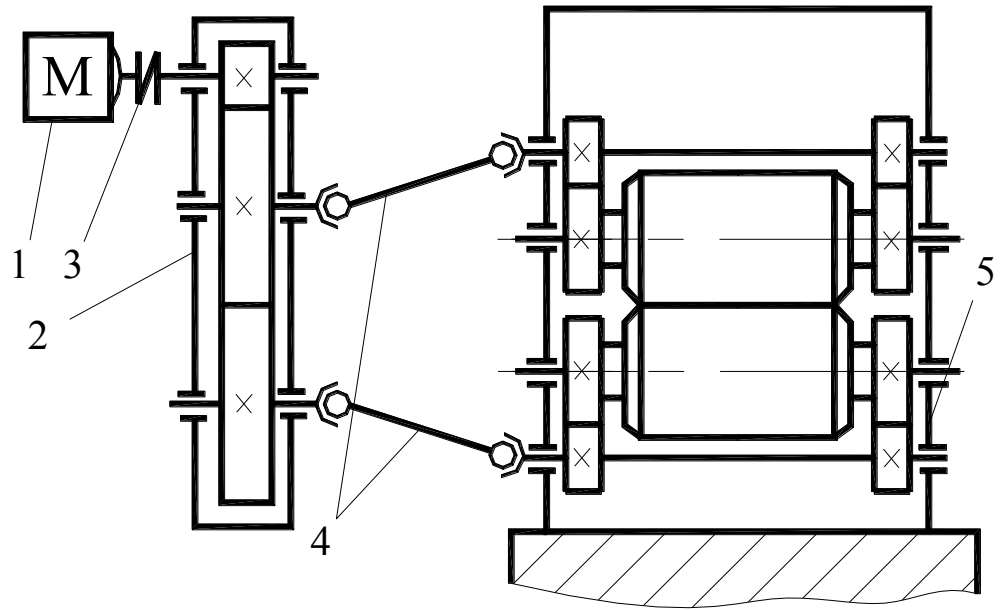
Кинематическая схема двухвалкового стана 600, предназначенного для прокатки листов из переработанных порошковых отходов подшипникового производства
